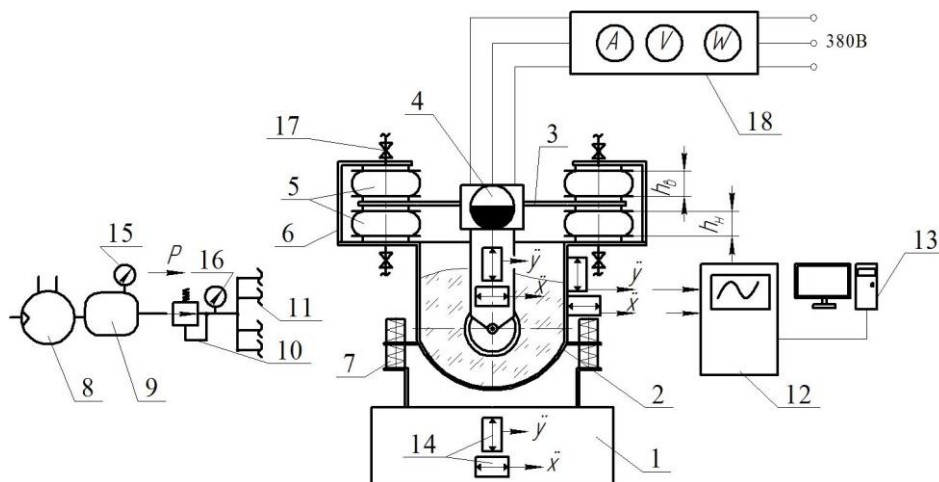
Конструкция виброупрочняющего станка ВУД-2500
